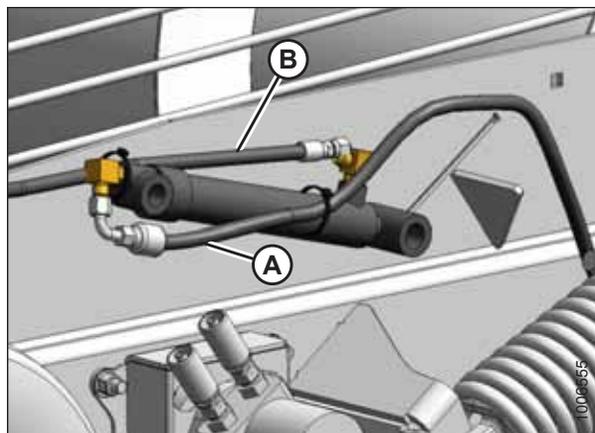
Cilindro maestro: lado izquierdo de la plataforma
